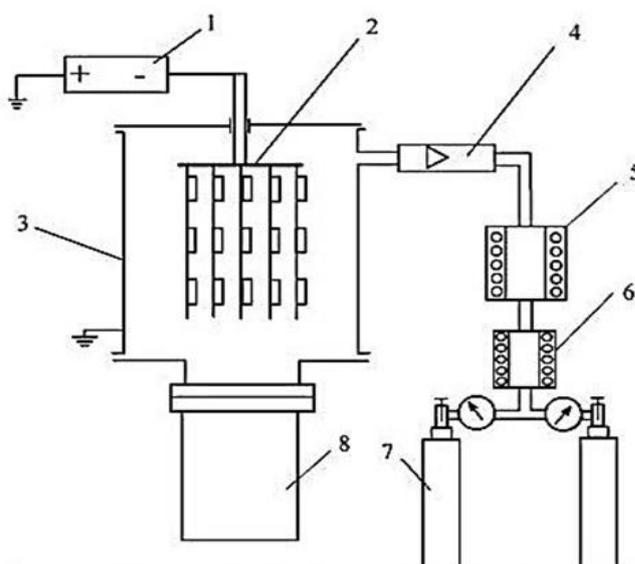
Схема вакуумной установки: 1 – источник питания; 2 – держатель с изделиями; 3 – вакуумная камера; 4 – ротаметр; 5,6 – фильтры; 7 – баллоны с газом; 8 – форвакуумный насос
